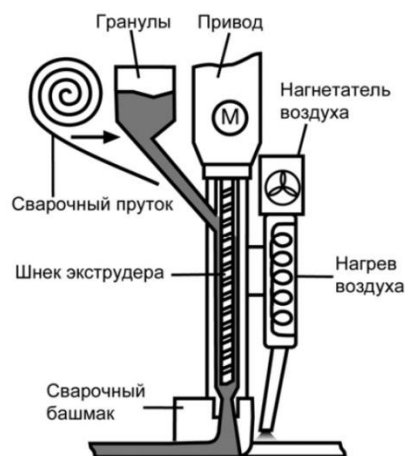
Схема работы сварочного экструдера.
